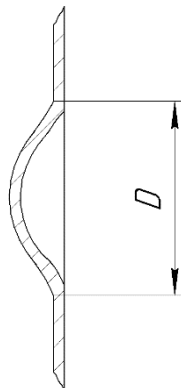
Профиль полусферической вмятины ферромагнитной заготовки
